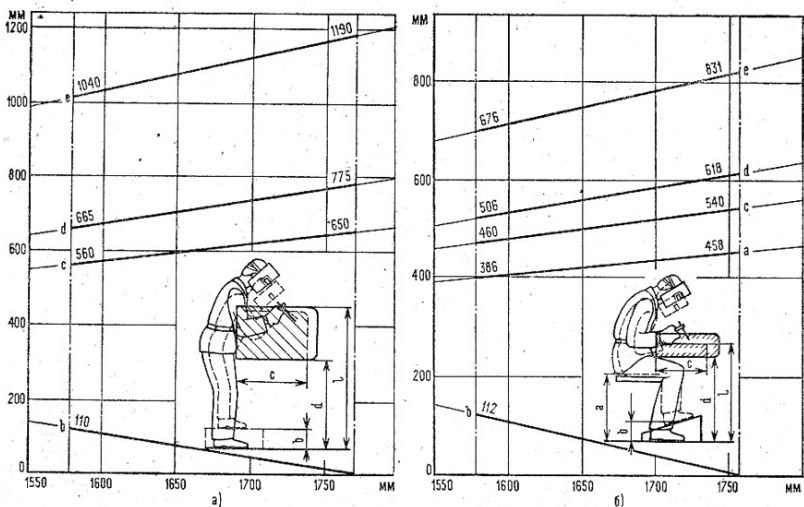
Параметры стационарного рабочего места сварщика при сварке: а) стоя; б) сидя
